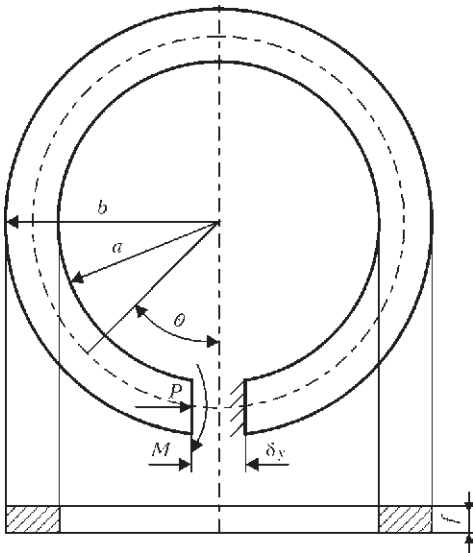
Схема нагружения кольца при контактной стыковой сварке
